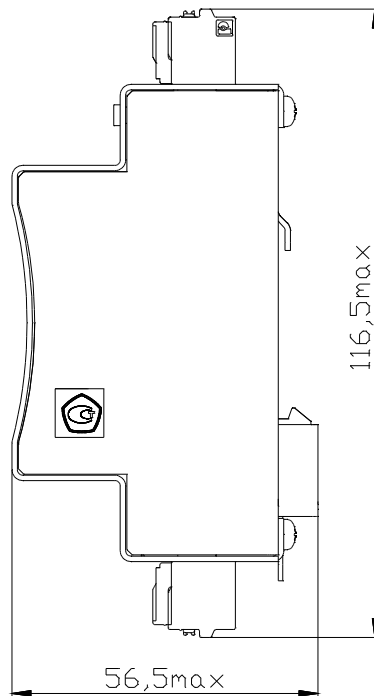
Модуль УВВ. Габаритный чертеж. Вид сбоку
